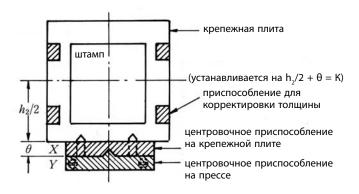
Верхнее и нижнее центровочное приспособление
